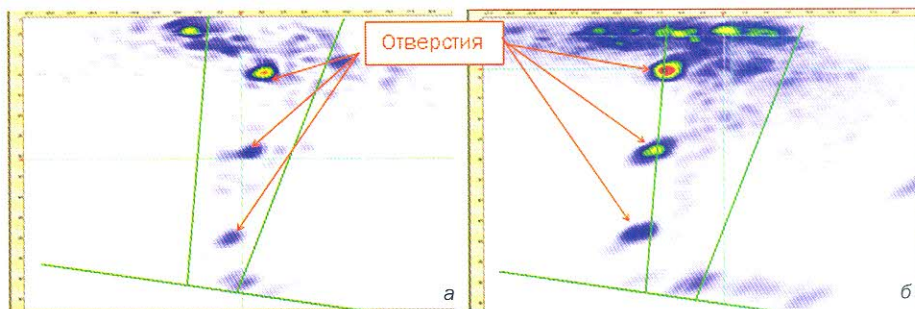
Схема контроля L60: а – три отверстия бокового сверления Ø2 мм в центре сварного шва; б – три отверстия бокового сверления Ø2 мм на кромке сварного шва (наложена маска сварного шва)
